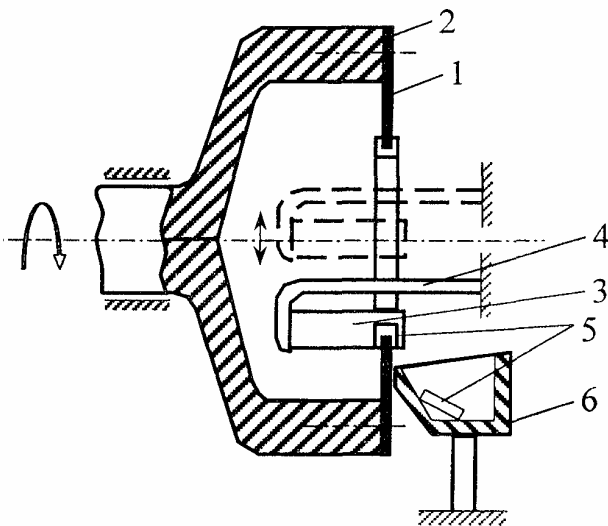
Схема різання кристалічної циліндричної заготовки кругом АКВР: 1 – круг АКВР, 2 – барабан, 3 – кристал, 4 – оправка, 5 – пластина, 6 – збірний лоток.
